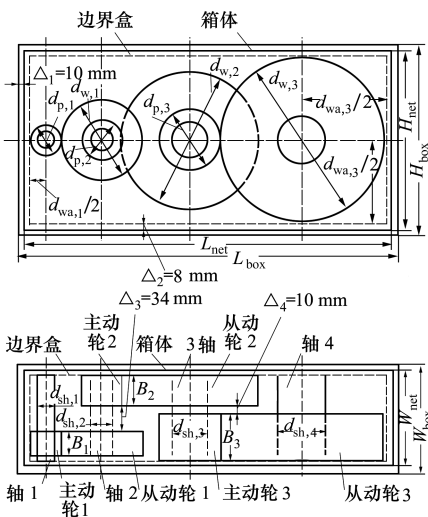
ZSY 型 3 级圆柱齿轮减速器常规设计结果的布局形式
